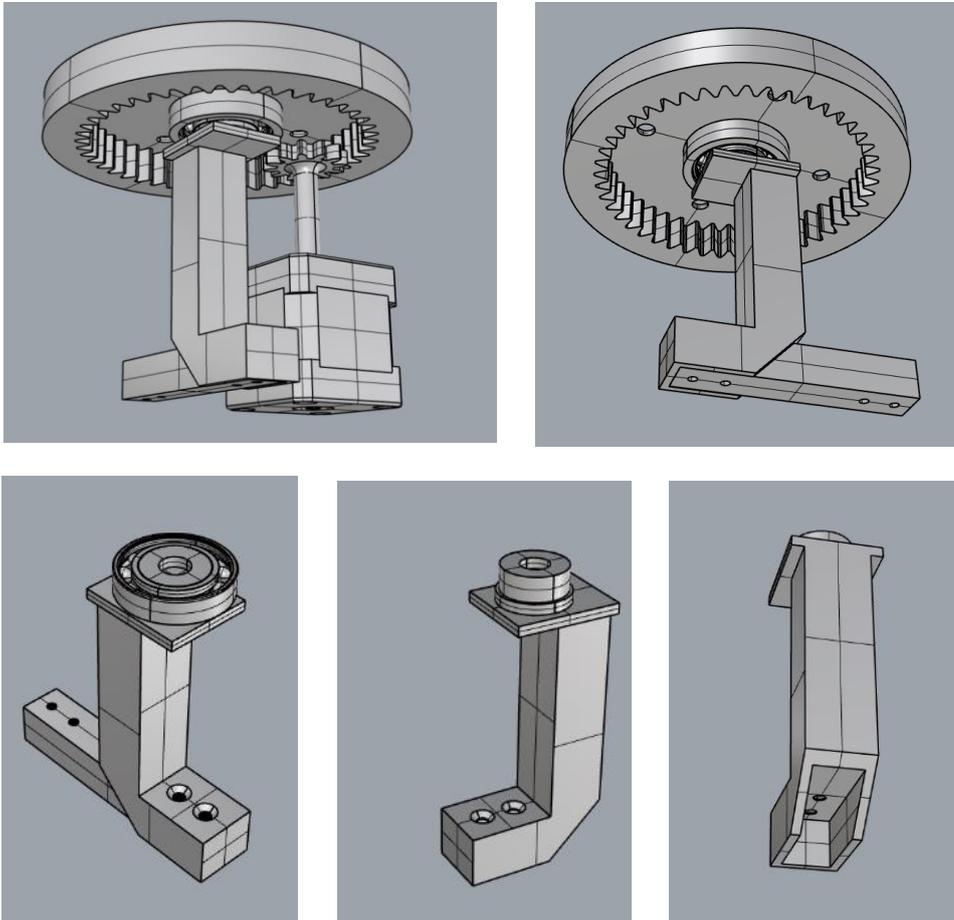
, 62b, 62c, 62d y 62e. Soporte rodamiento.
